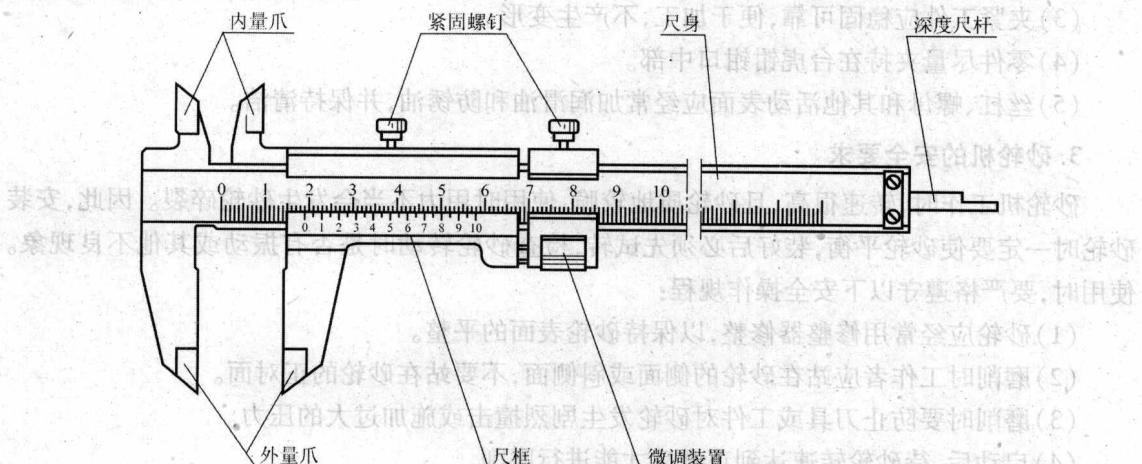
游标卡尺的构造(准确度为 0.025mm)
